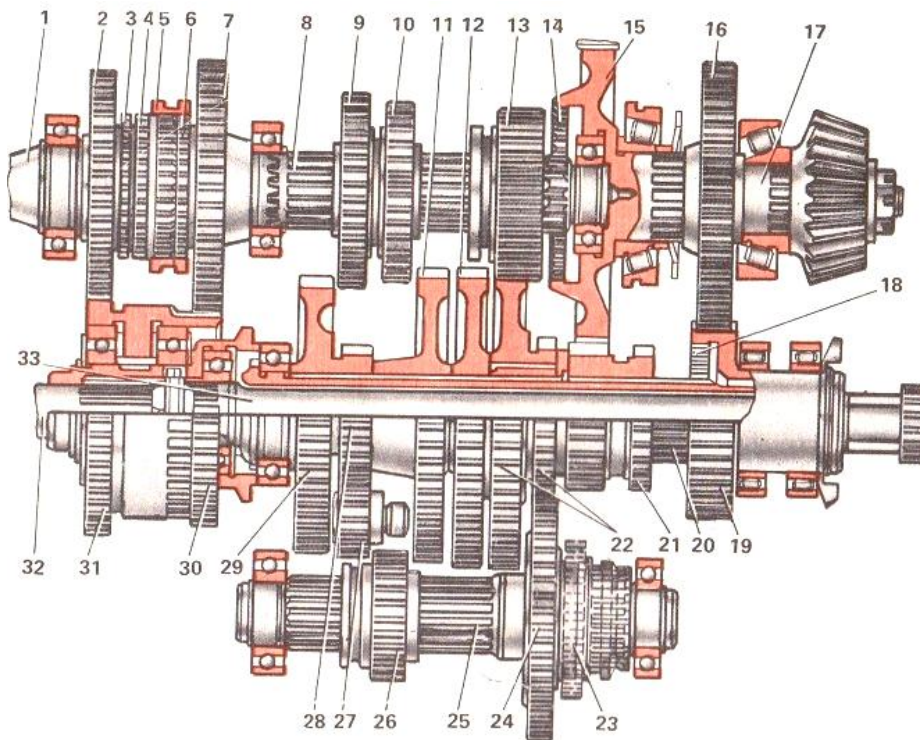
Коробка передач трактора МТЗ-80
